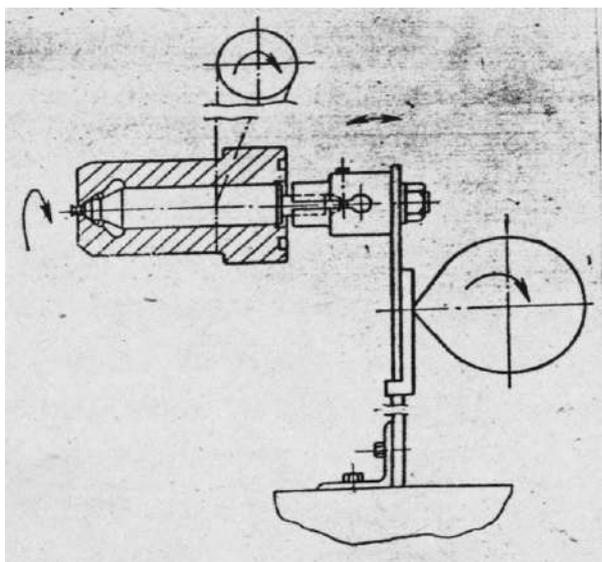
Схема станка для взаимной притирки (спаривания) иглы с корпусом распылителя по запирающему конусу
